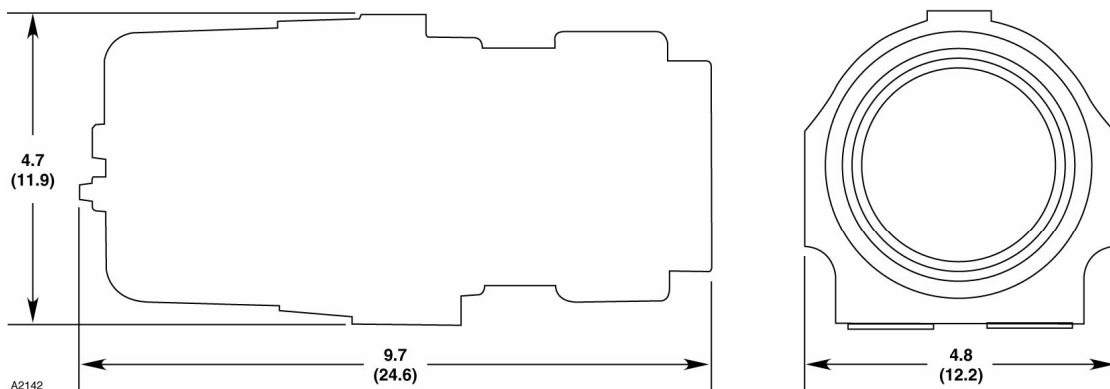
Габаритные размеры извещателя в дюймах (см).
